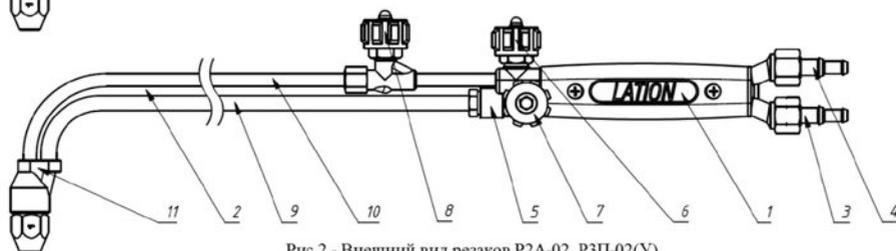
Внешний вид резаков P2A-02, P3П-02(У)
